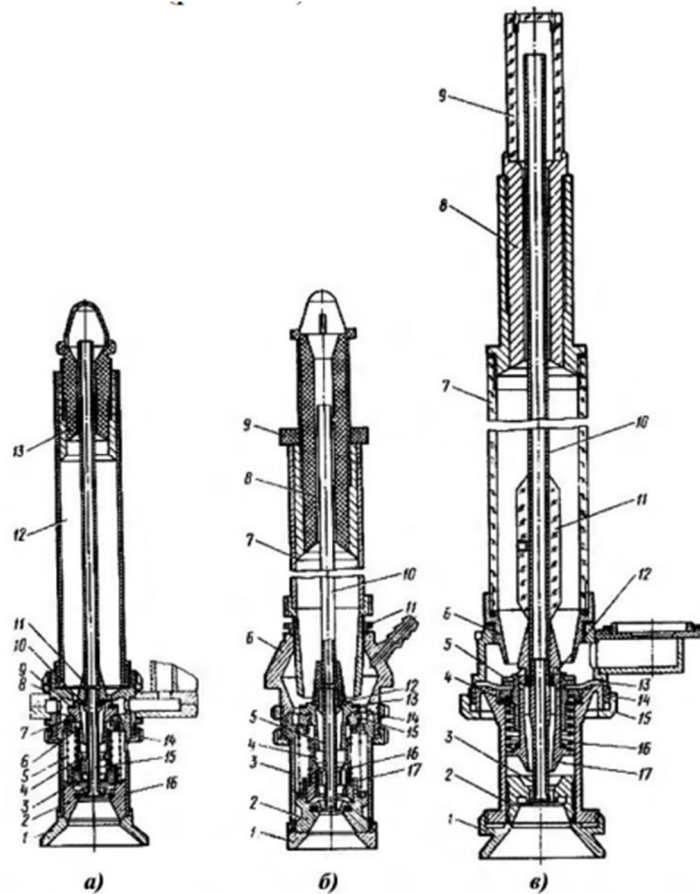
Фасувальні пристрої машин рідкої продукції: *а* – ВАР-6; 1 – дзвіночок; 2 – вкладка; 3 – поршень; 4, 5 – пружина; 6 – заливна трубка; 7 – гумова мембрана; 8 – корпус; 9, 10 – клапани; 11, 14 – гайки; 12 – мірний стакан; 13 – витискувач; 15 – шатрова трубка; 16 – стакан; *б* – Д9-ВР2М-6; 1 – дзвіночок; 2 – вкладка; 3 – стакан; 4 – поршень; 5, 10 – трубки; 6 – корпус; 7 – мірний стакан; 8 – витискувач; 9 – гайка; 11 – контргайка; 12, 13 – клапани; 14 – зливна втулка; 15 – мембрана; 16, 17 – пружини; *в* – Т1-ВНА-12; 1 – дзвіночок; 2 – вкладка; 3 – шатрова трубка; 4 – зливна втулка; 5, 12 – клапани; 6 – сидло клапана наповнення; 7 – мірний стакан; 8, 11 – витискувач; 9 – ковпачок; 10 – трубка; 13 – мембрана; 14 – корпус; 15 – накидна гайка; 16 – пружина; 17 – стакан
